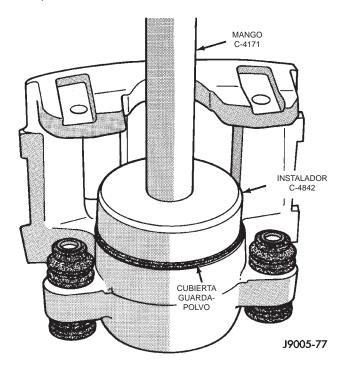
Instalación de la cubierta guardapolvo del pistón
